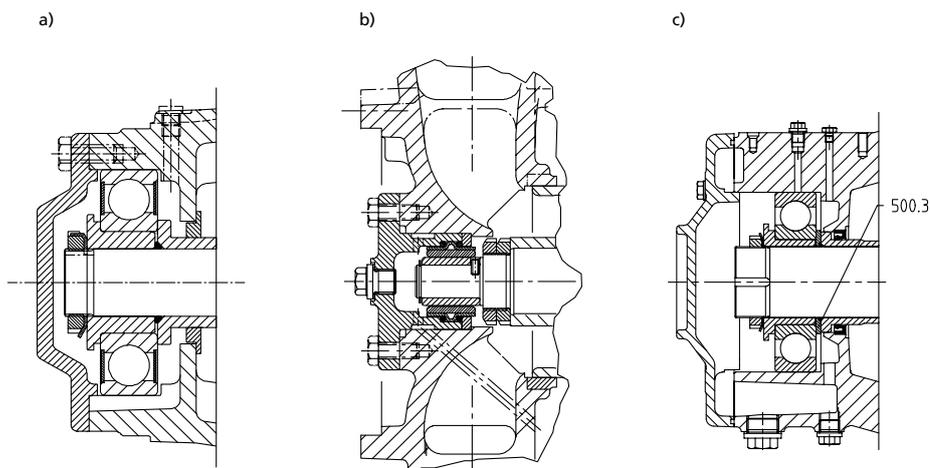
а) радиальные шарикоподшипники в качестве плавающих подшипников, типоразмеры 32-200 - б) подшипники скольжения в качестве плавающих подшипников- в) радиальные шарикоподшипники в качестве плавающих подшипников, типоразмер 250
